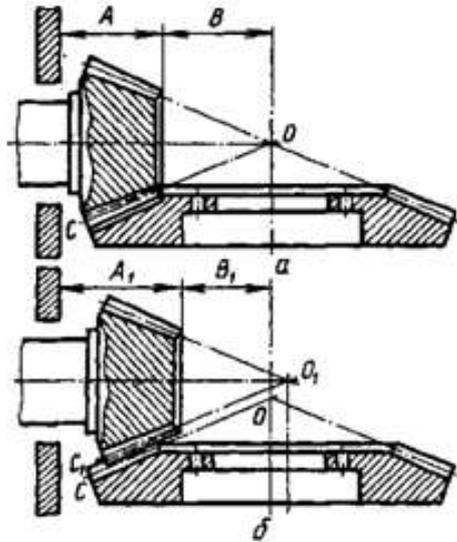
Схема регулировки зацепления зубчатых колес главной передачи:
